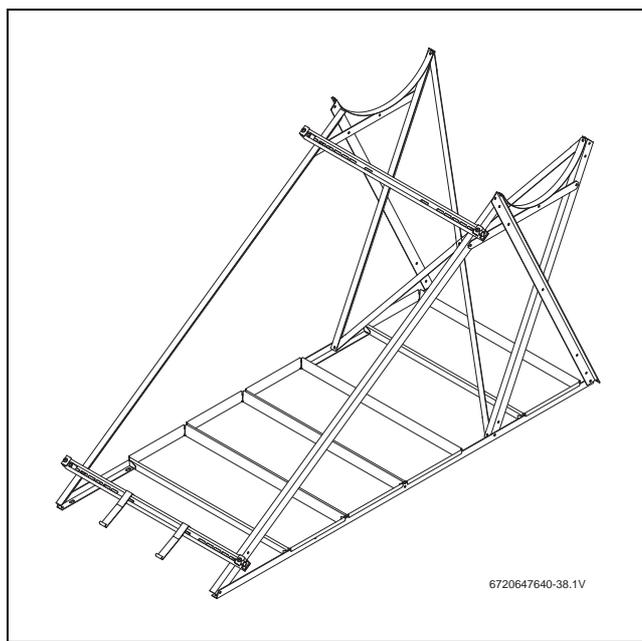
Estrutura para telhado plano fixa através de placas de betão, medidas em mm (aqui no sistema de 150/200 I)
